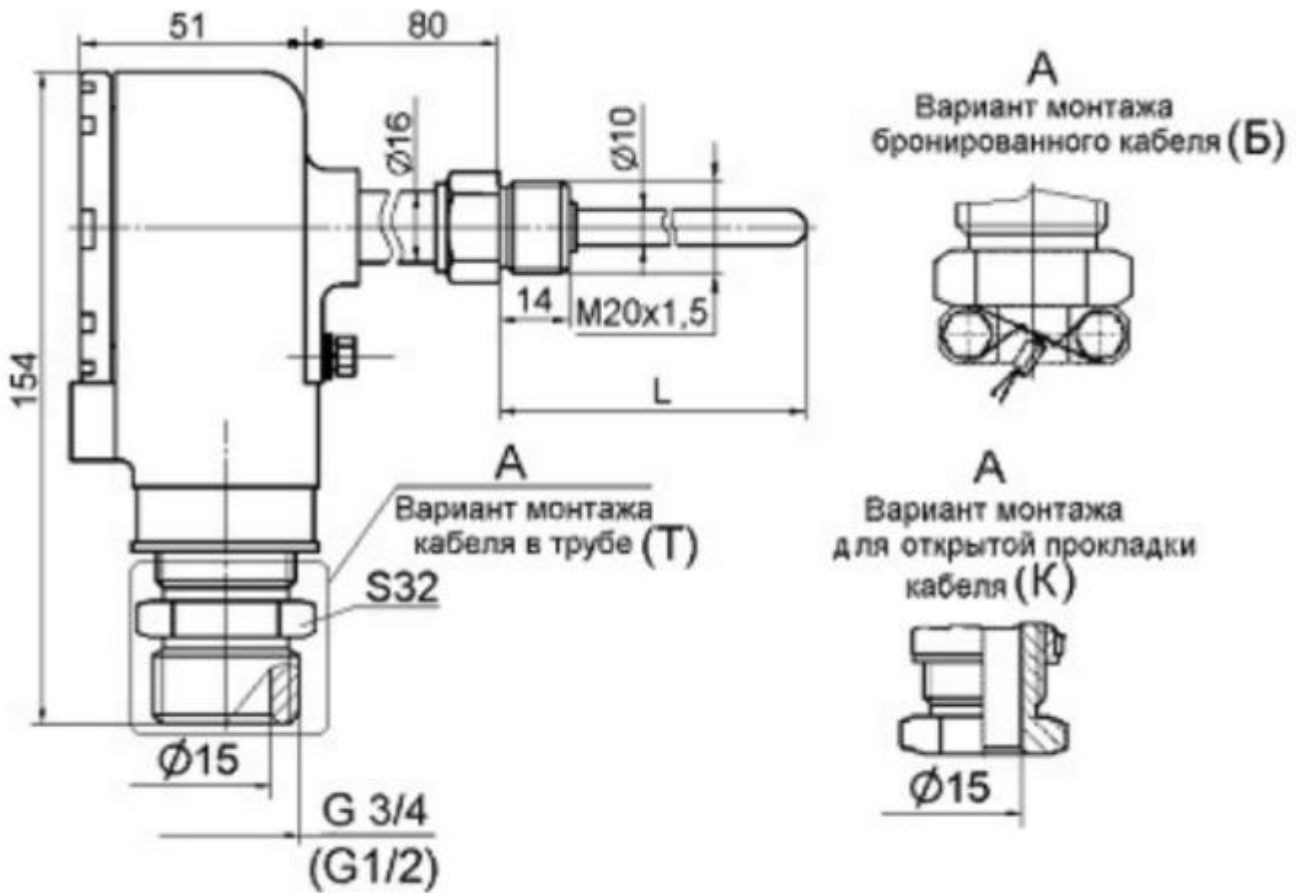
Головка из алюминиевого сплава. Штуцер неподвижный
